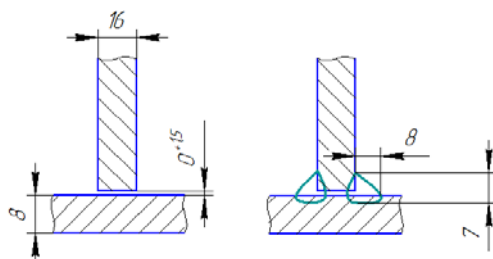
Форма и размеры сварного соединения типа Т-3 по ГОСТ 14771-76.
